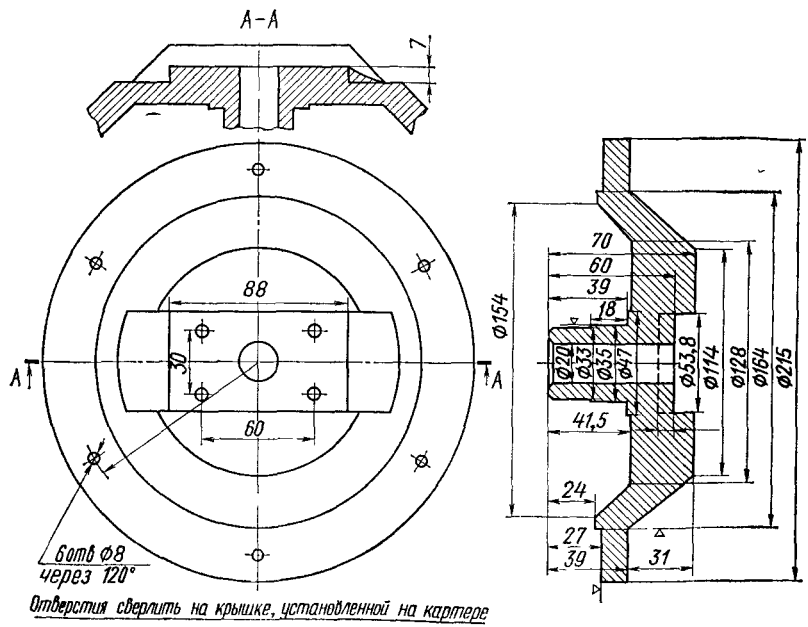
Подготовка картера главной передачи для установки увеличенных шестерен:
